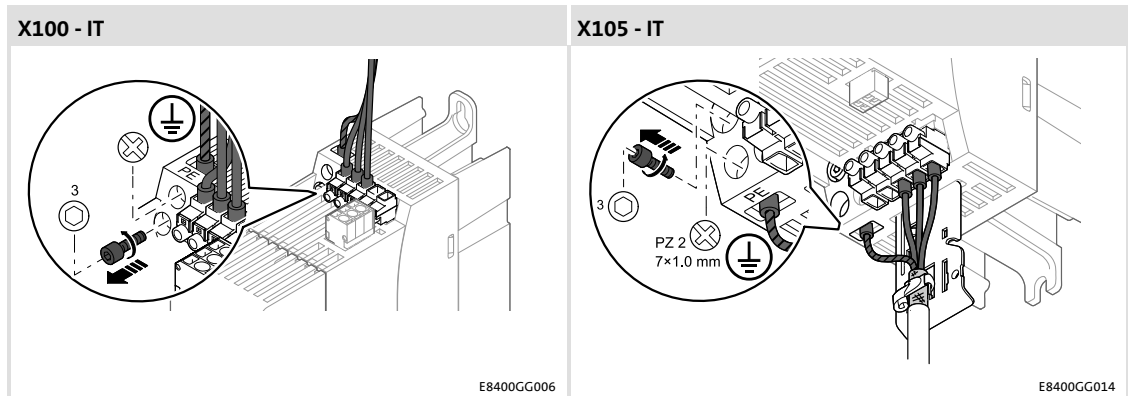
Entfernen der Kontaktschrauben bei Gerätegröße 1 ... 3 (netzseitig und motorseitig)
